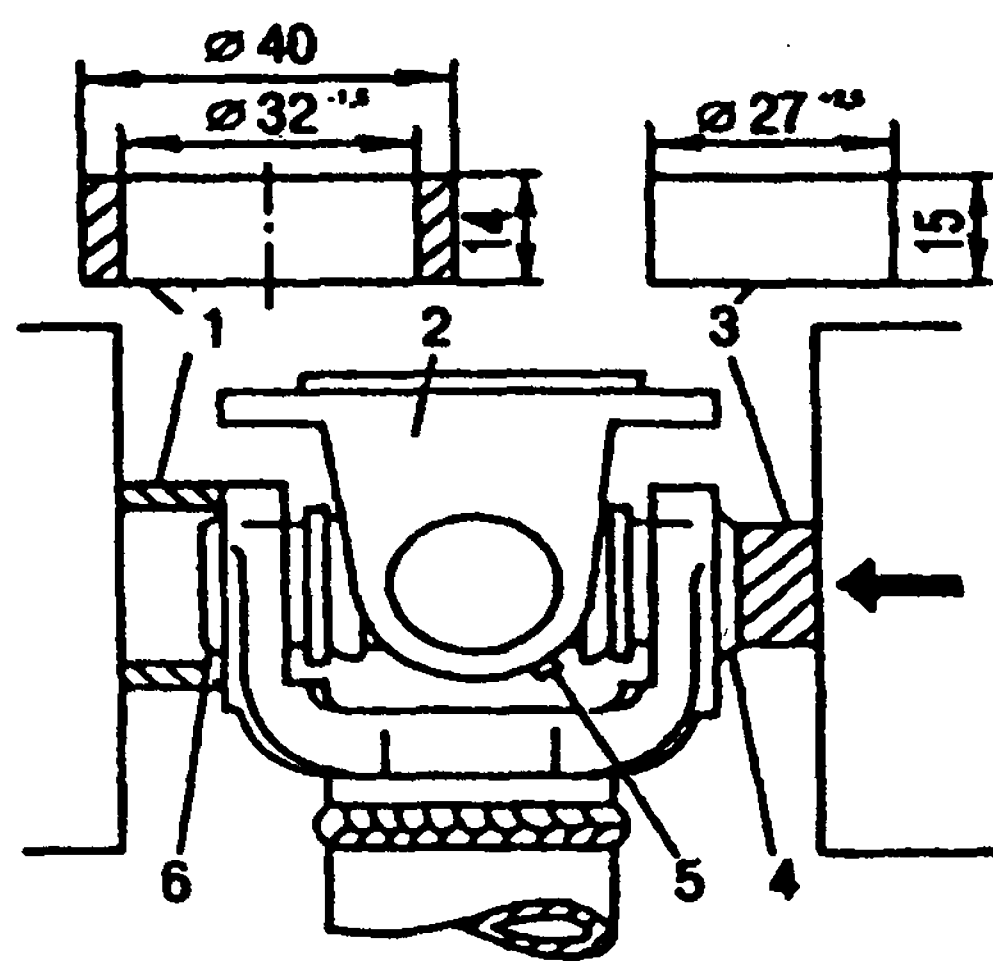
Разборка карданного шарнира: 1 - кольца; 2 - фланец шарнира карданной вала; 3 - оправка; 4 и 6 - подшипники; 5 - масленка
